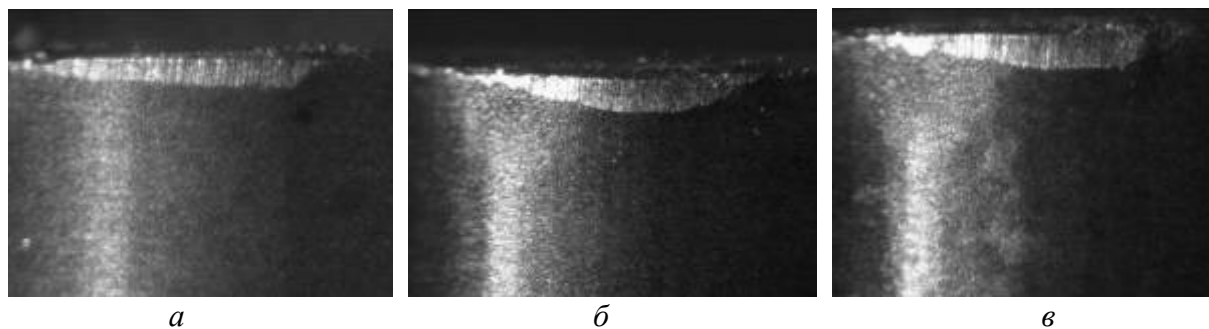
Внешний вид износа на задней поверхности пластин, изготовленных из керамики различных марок, при точении стали ШХ15 с подачей 0,05 мм/об: а – ZIRCA; б – CC650; в – BOK-71
